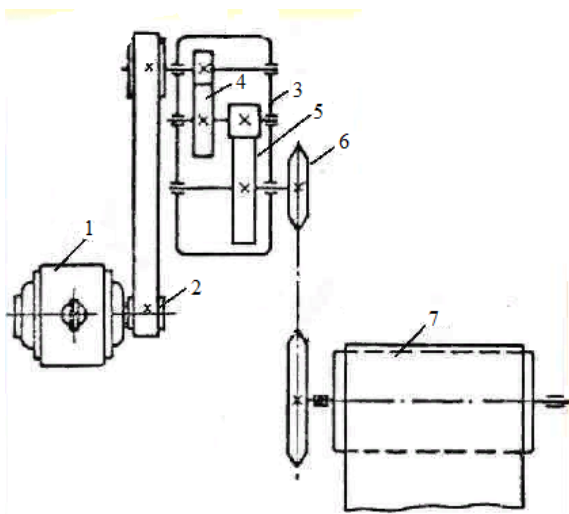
Привод ленточного транспортера: 1 – электродвигатель; 2 – ременная передача; 3 – двухступенчатый цилиндрический редуктор; 4 – цилиндрическая быстроходная ступень; 5 – ступень цилиндрическая тихоходная; 6 – цепная
